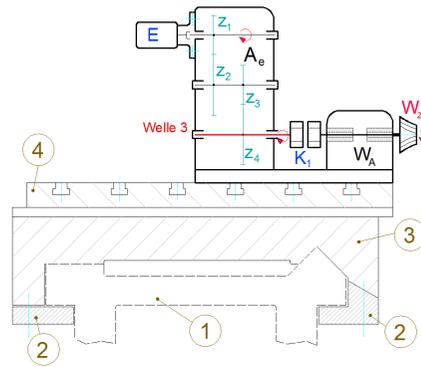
Prinzipskizze eines Fräswerkzeugs zum Freischneiden
